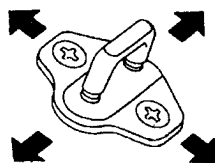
Регулировка положения фиксатора (См. Раздел 13)
